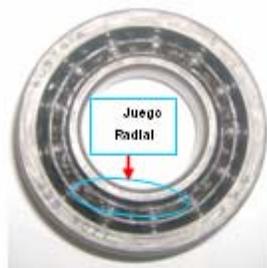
1: Rodamiento del lado motriz del motor. [Fuente: Propia]
